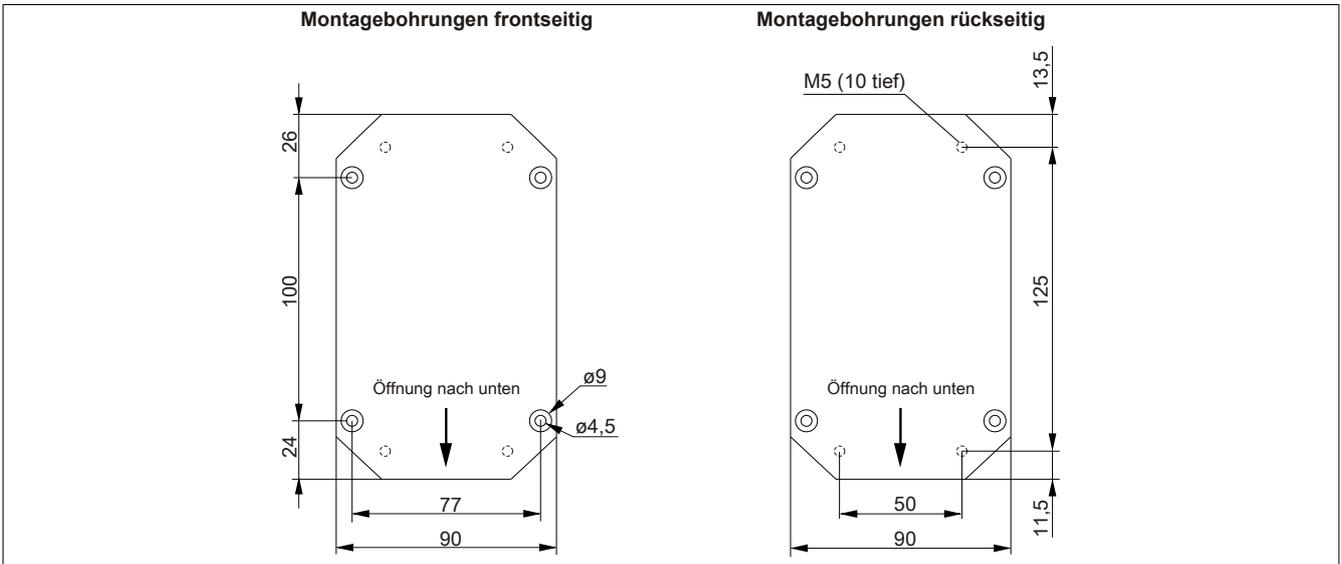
4MPCBX.0000-01 - Bohrschablone
